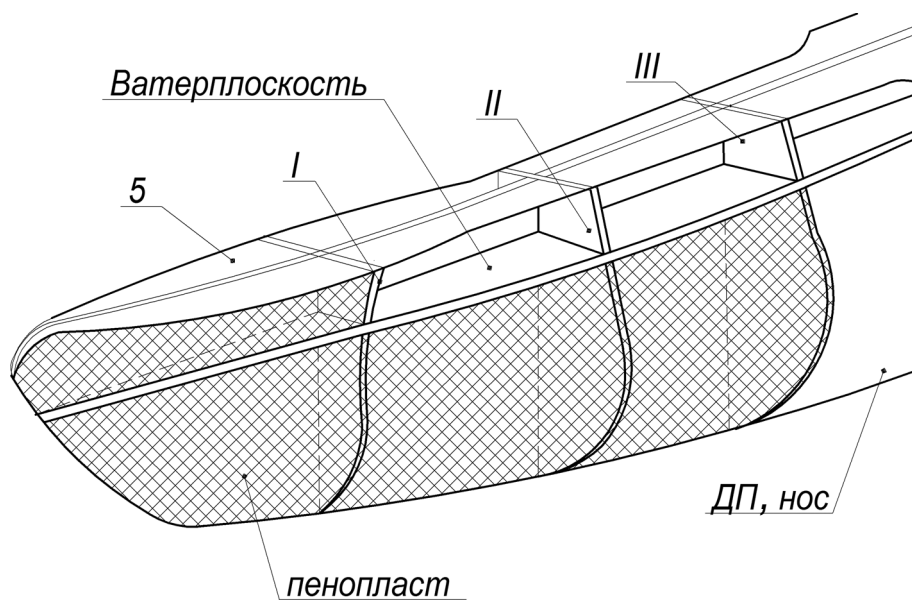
Схема заполнения пенопластом носовой части корпуса.
